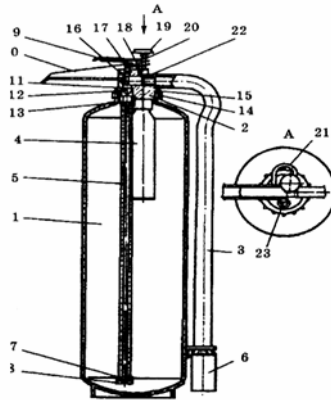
Вогнегасник повітряно-пінний ОВП- 10: 1 - корпус; 2 - головка; 3 - рукав; 4 - балон з робочим газом; 5 - трубка сифона; 6 - піногенератор; 7 - сітка; 8 - корпус фільтра; 9 - важіль керування клапаном; 10 - ручка; 11 - кільце ущільнювача; 12 - клапан; 13 - перехідник; 14 - гайка накидна; 15 - кільце ущільнювача; 16 - штифт; 17 - пружина; 18 - вісь; 19 - кнопка з голкою; 20 - пружина; 21 - запобіжна чека; 22 - кільце ущільнювача; 23 - запобіжний клапан.
